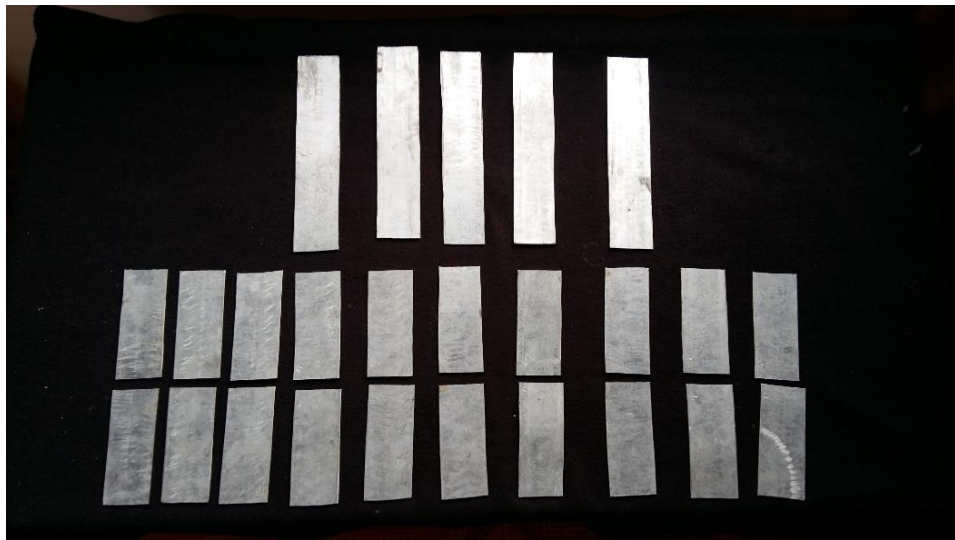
Corte de las placas para soldadura a tope.
